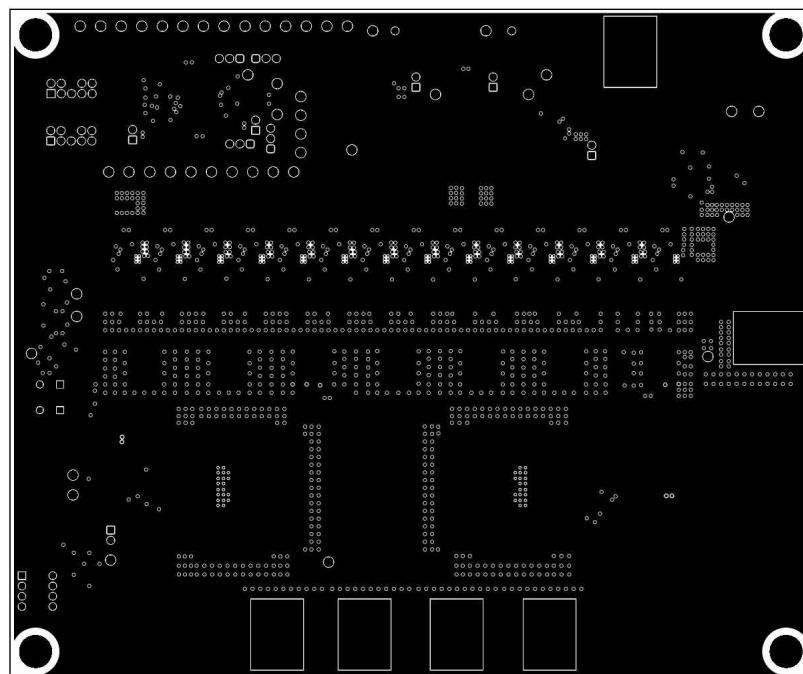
TPS53676EVM-084 PCB 第 2 层 - GND
